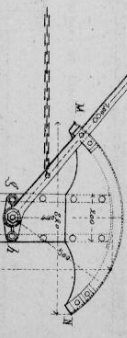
Plan du côté M du poteau de manœuvre (1/5)
